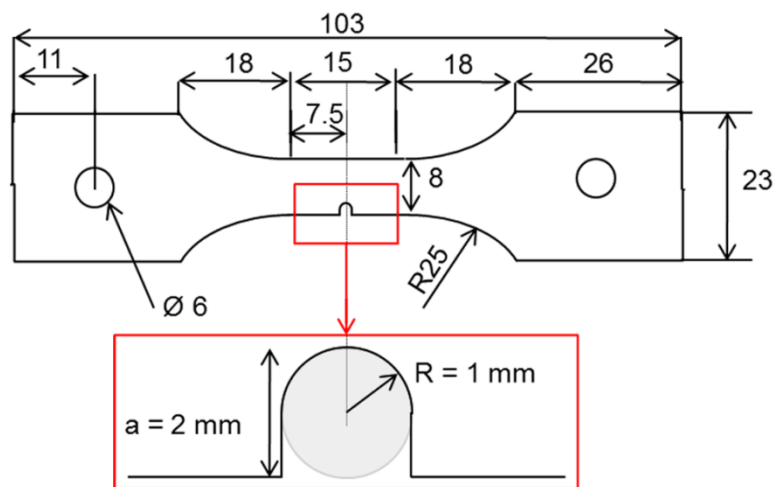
Schéma des éprouvettes de fatigue entaillées.
